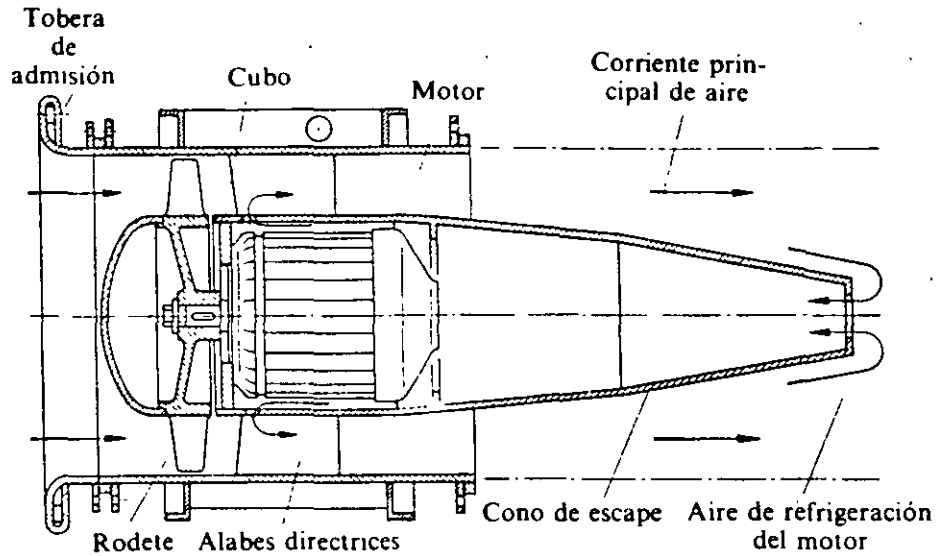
Ventilador axial de aire construido por la casa Siemens para ventilación de minas para 2.900 rpm y elevado rendimiento (80 %).
